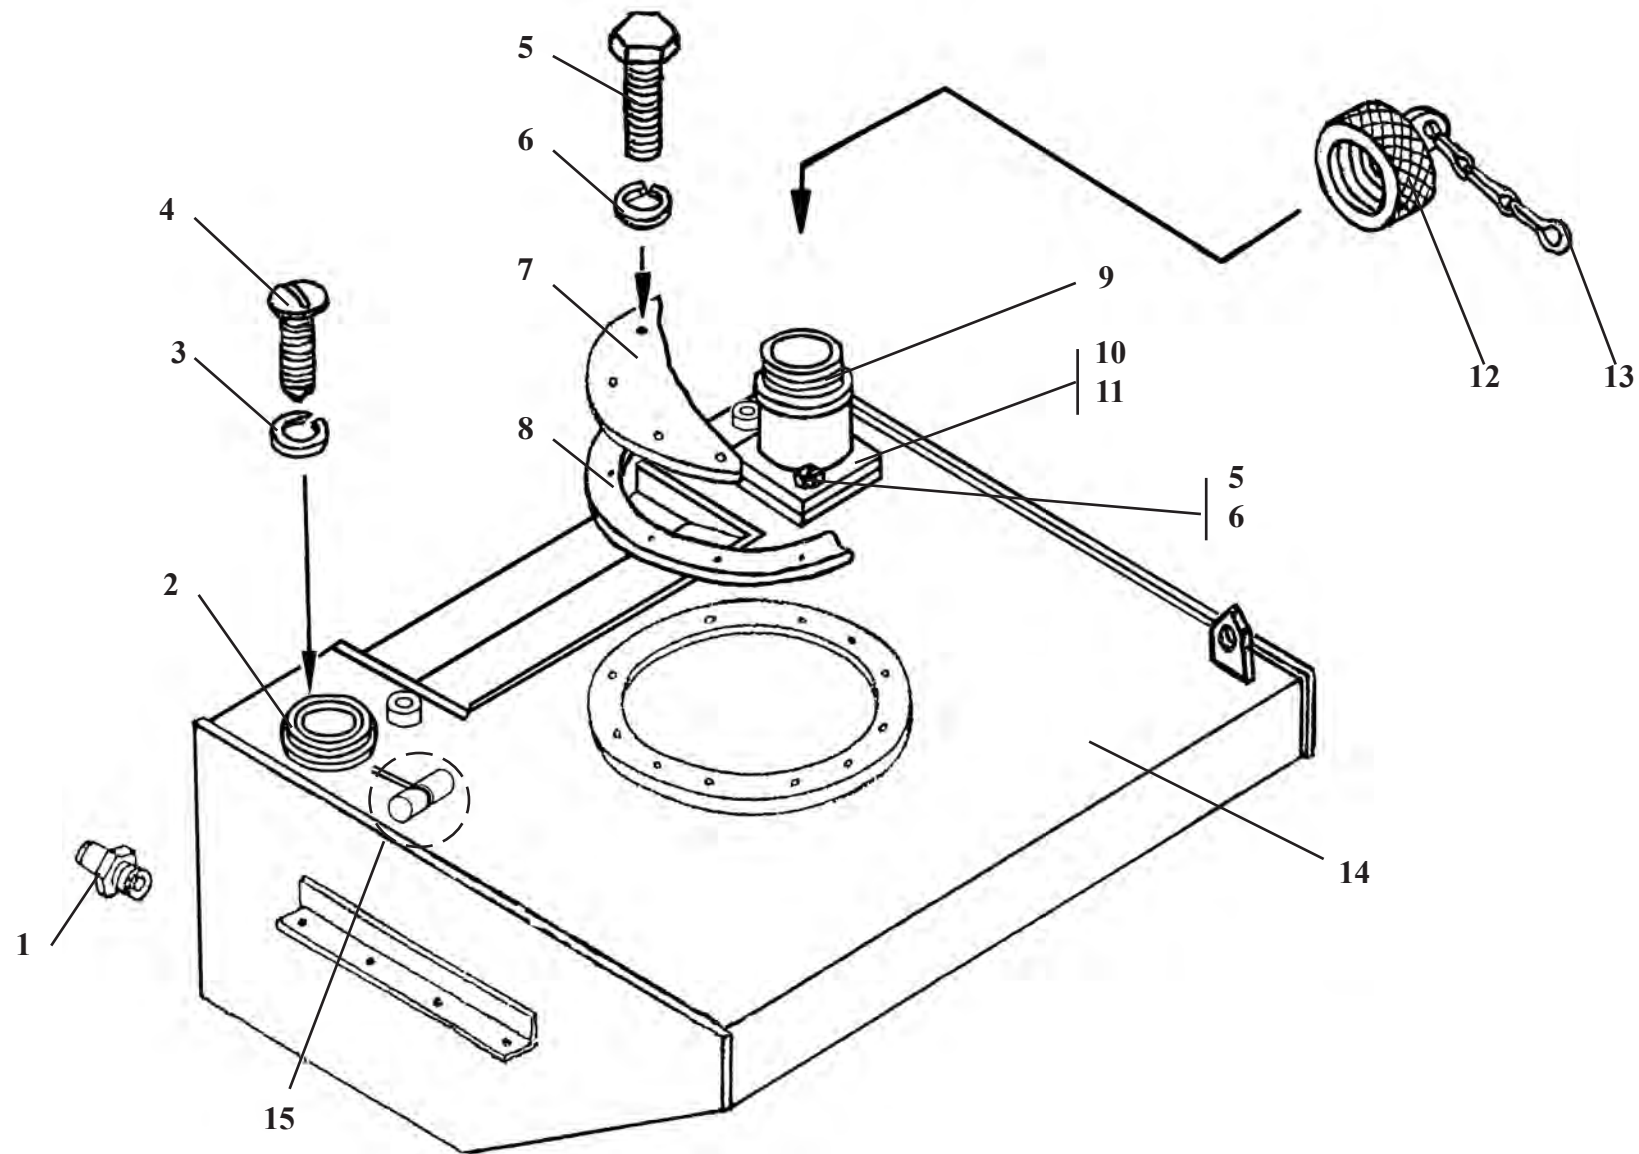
ТО-28А.02.02.000	Бак топливный
